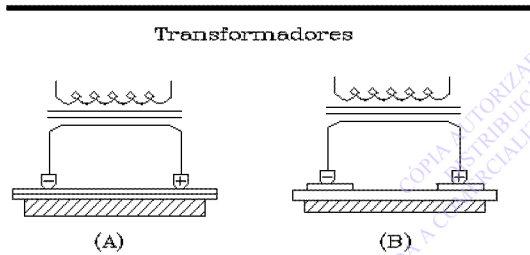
Soldagem com Conexão Elétrica em Série.
